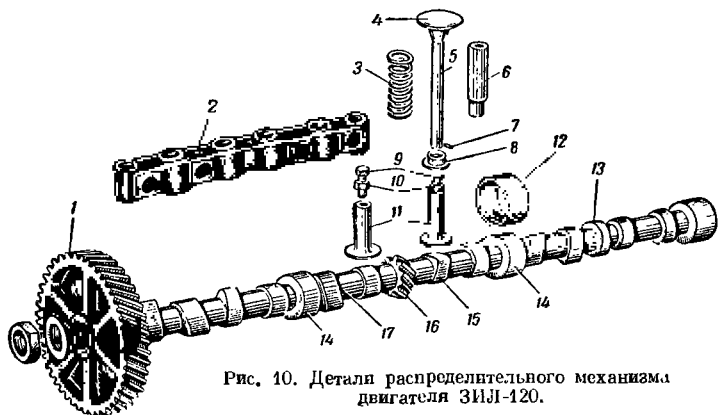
Детали распределительного механизма двигателя ЗИЛ-120.
